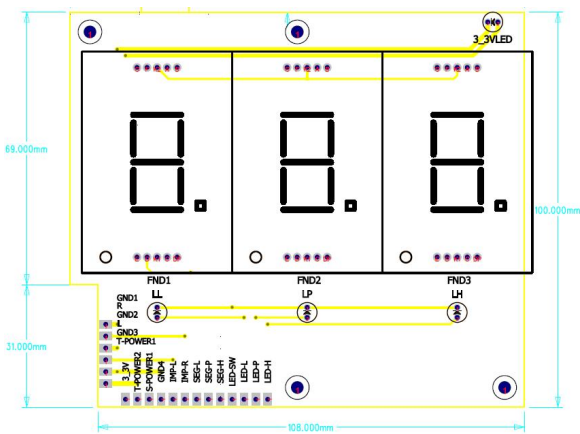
이어폰 기능 검사장치의 모니터 PCB 보드
